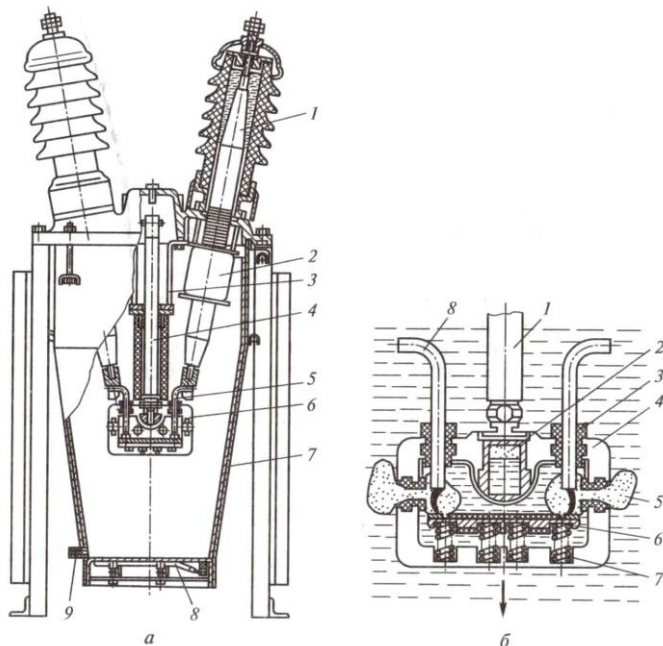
Выключатель баковый масляный С-35-630-10:
